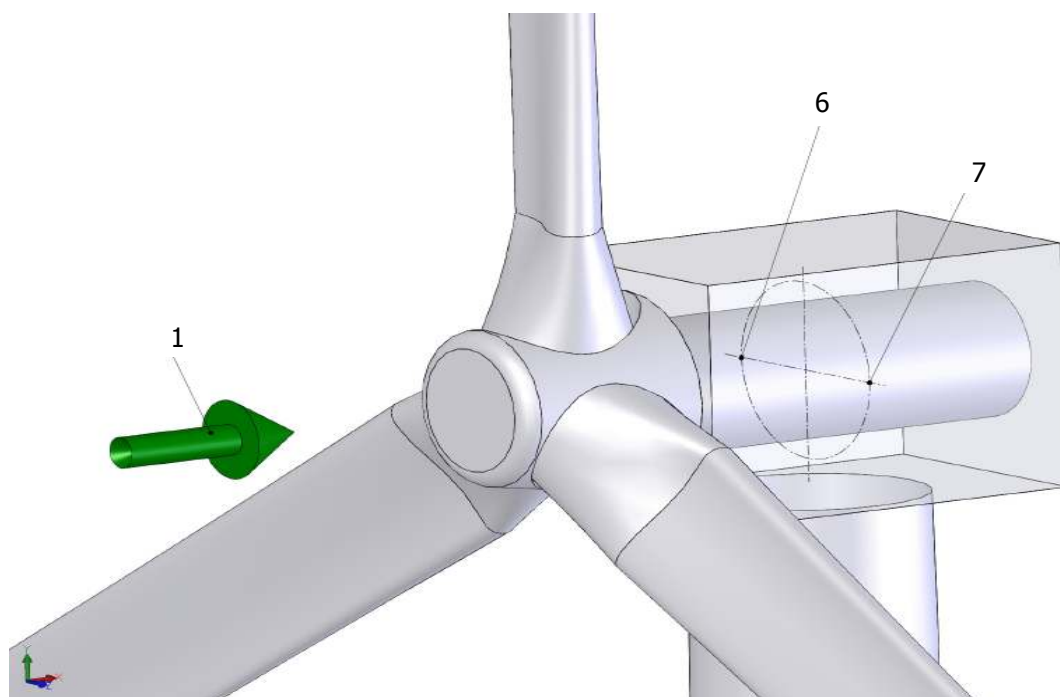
Posición típica del punto de deslizamiento en la rodapiés principales
